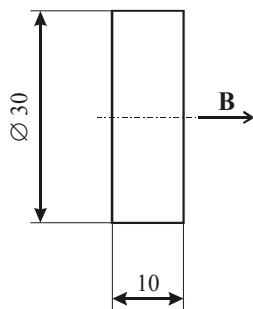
Внешний вид и габаритные размеры датчиков серий 290xxx и 303xxx
